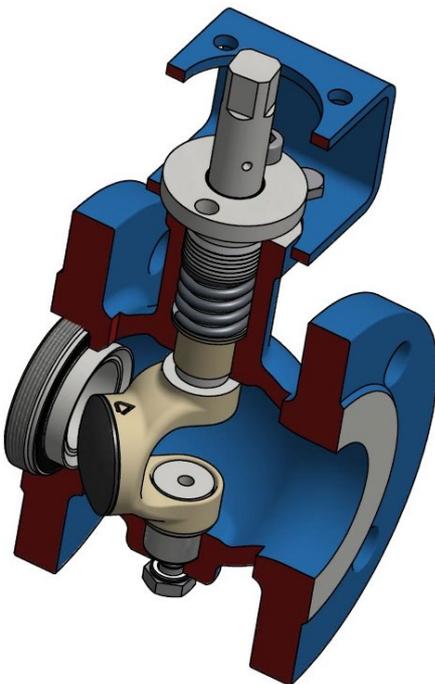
Zusammenbauzeichnung Ventil Typ 62.7
